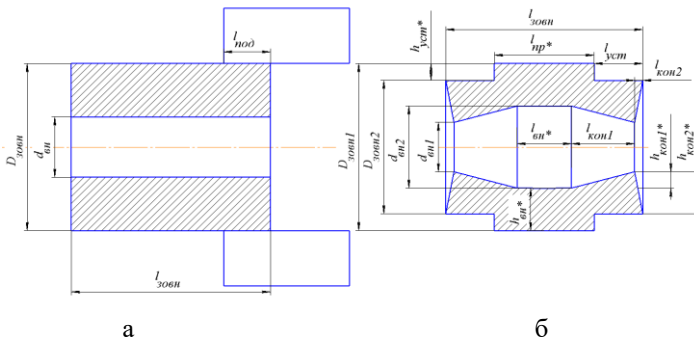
Загальний вигляд заготовки та поковки запірної арматури при куванні (а - заготовка, б - поковка)
